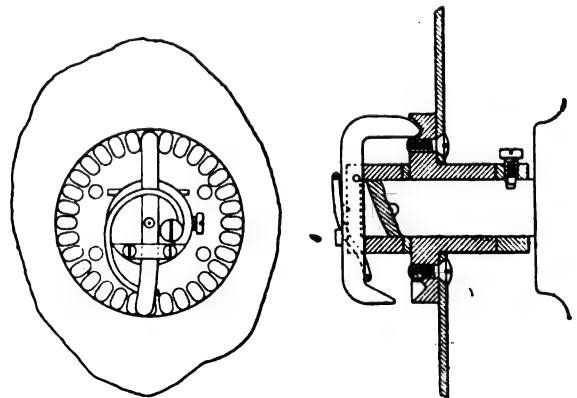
Dispositif employé pour décaler le disque mobile.
